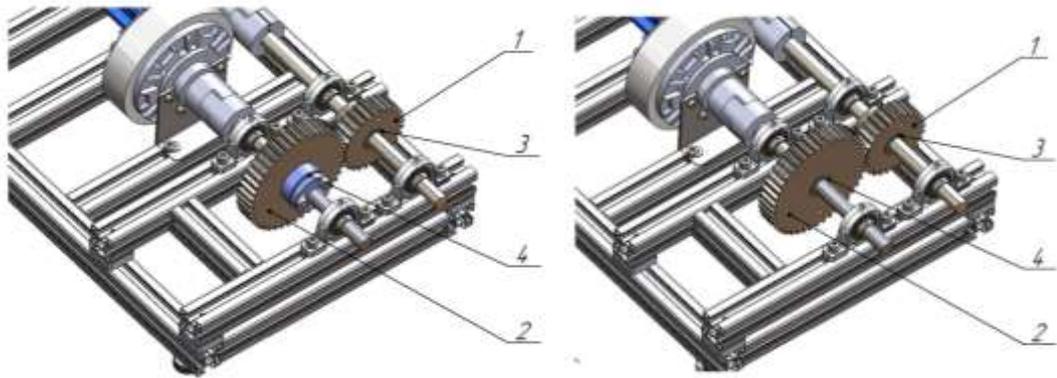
Установка зубчатых колес с использованием конических закрепительных втулок и цилиндрических втулок
